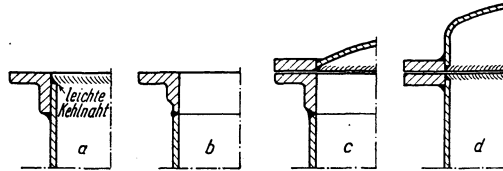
Schweißnähte an Winkelringen.
